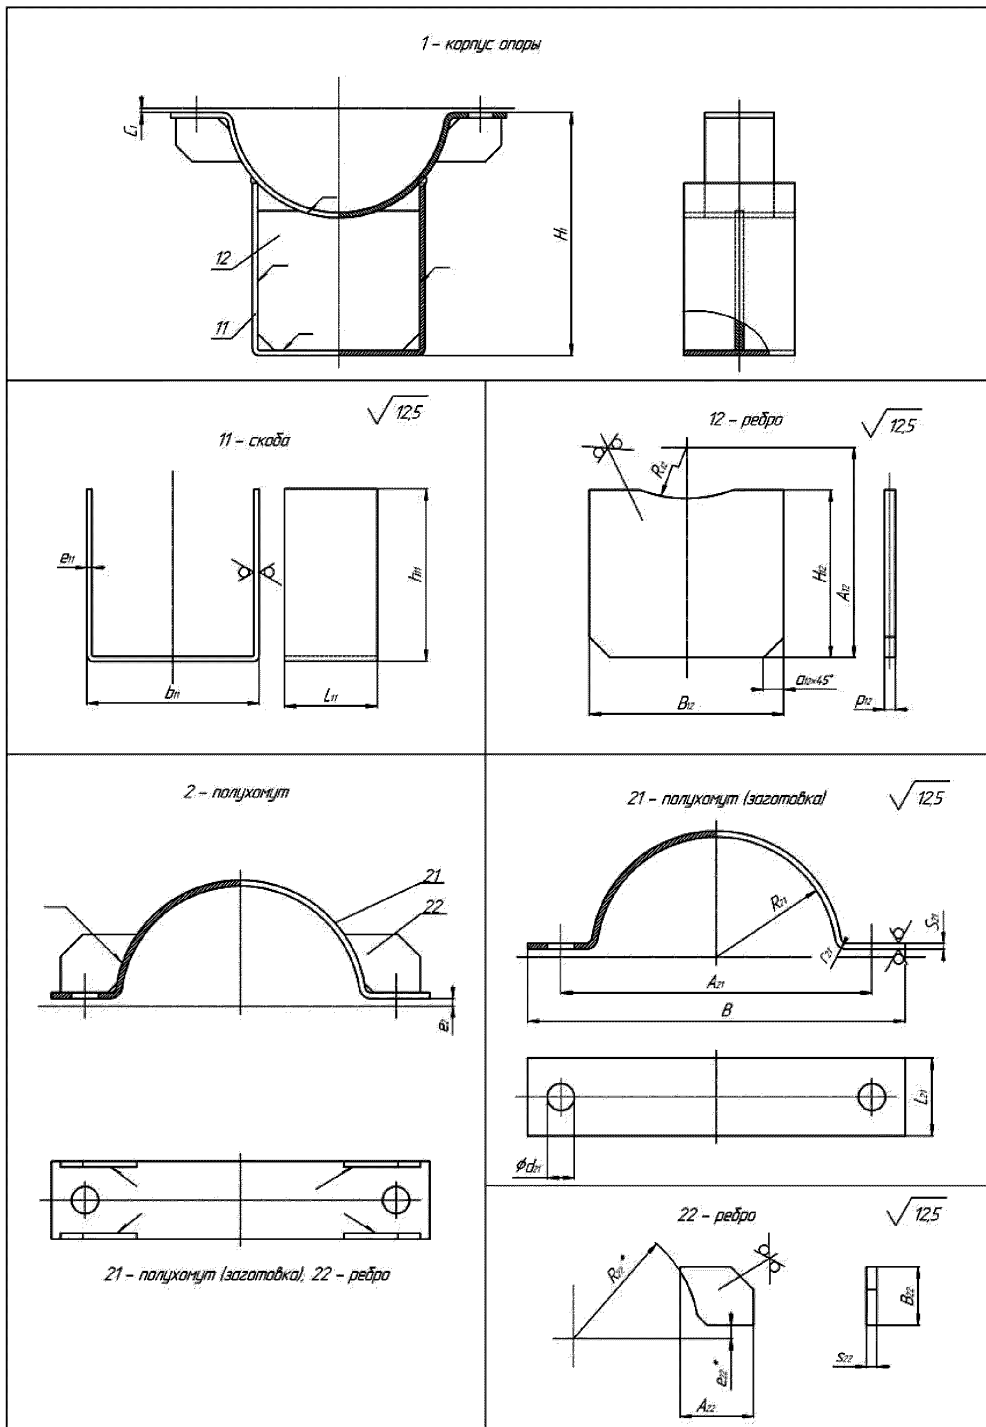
Детали изделий 01-XXXX-S-1C-03-A,
